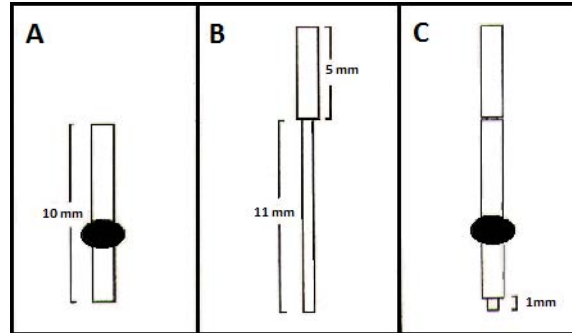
Dibujo esquemático acerca de los tamaños de la cánula guía y estilete. A) Punto negro hace referencia a la soldadura estaño en la cánula guía B) Estilete C) Estile insertado en la cánula guía, evitando la obstrucción de ésta. Fuente?
